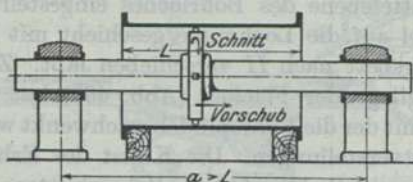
Plan einer Ausbohrmaschine mit wanderndem Bohrkopf.
